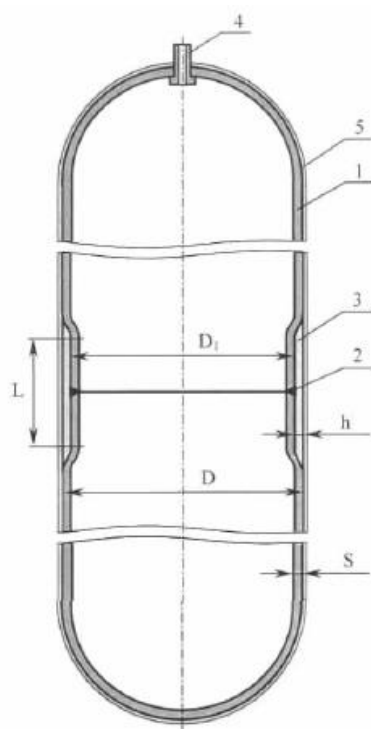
Схема балону високого тиску, що містить герметичний корпус виготовлений з двох півбалонів
